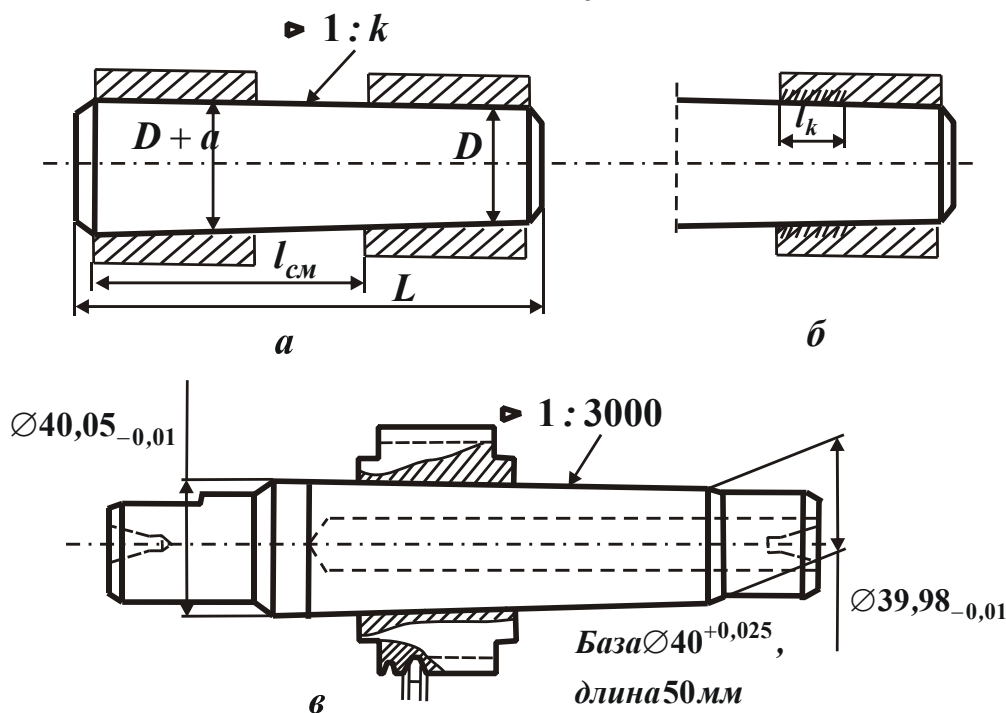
Схема базирования заготовки с главной базой, имеющей вид цилиндрического отверстия, на наружную коническую поверхность.
